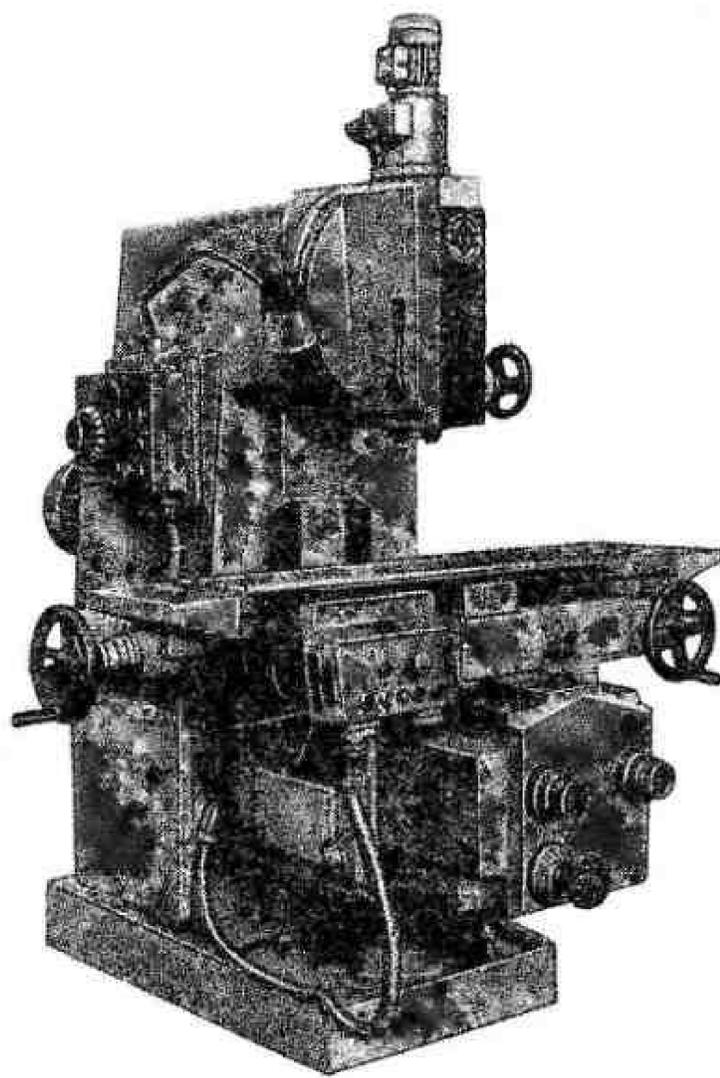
Вертикальный консольно-фрезерный станок 6Т13-1
